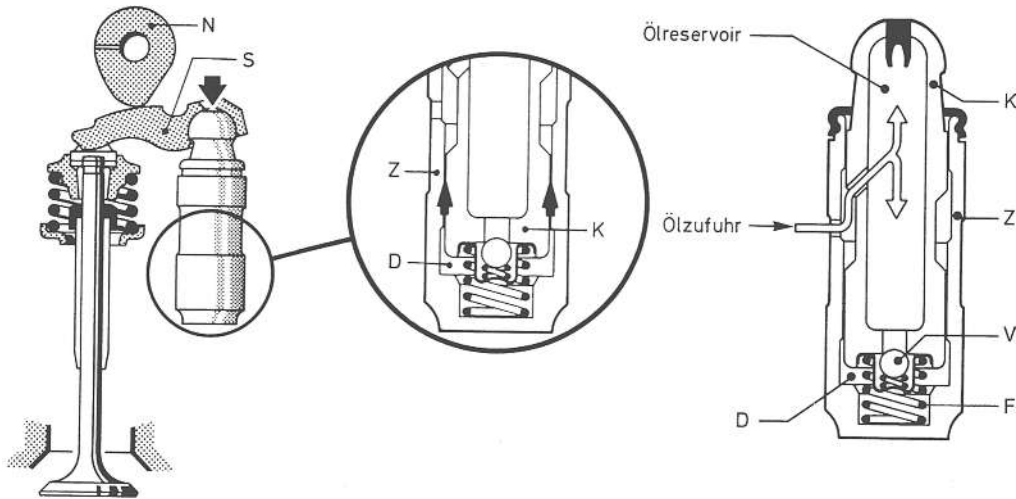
Hydraulischer Ventilspielausgleicher am Motor eines Opel. Beim Öffnen des Ventils tritt eine geringe Leckölmenge zwischen Kolben (K) und Zylinder (Z) aus dem Druckraum aus (Pfeile in der Ausschnittvergrößerung).
